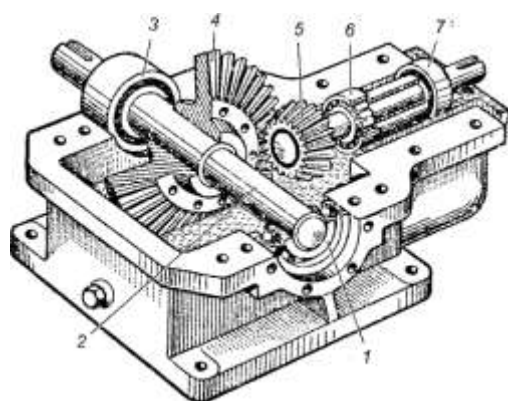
Конический редуктор: 1, 3 — подшипники ведомого вала; 2 — ведомый вал; 4, 5 — конические зубчатые колеса; 6, 7 — подшипники ведущего вала
